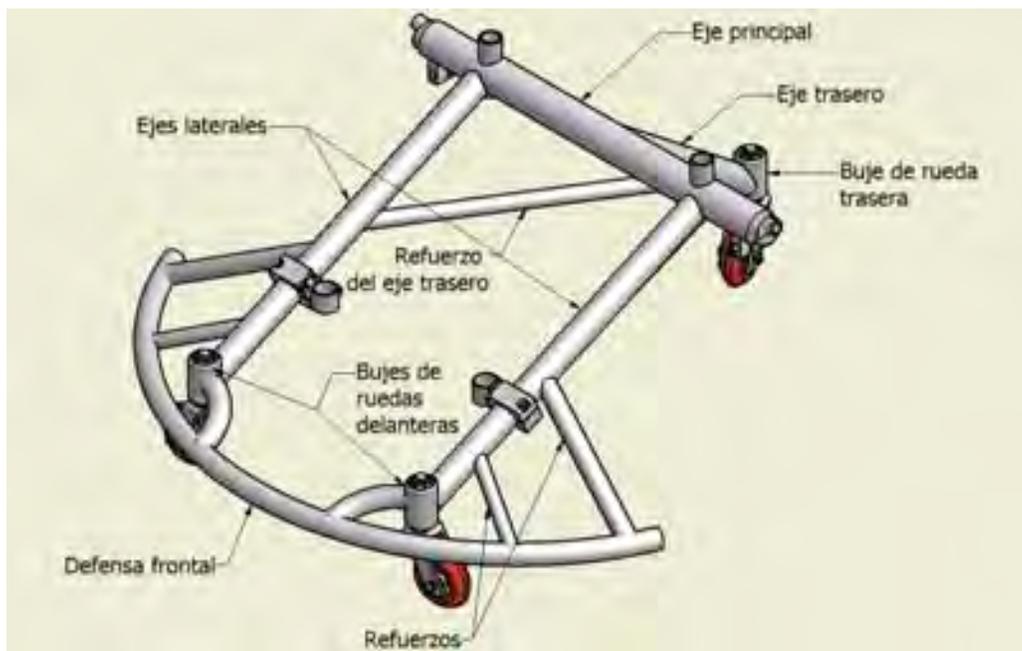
Base principal de la silla de ruedas de balón cesto. Esta estructura se encuentra unida por medio del proceso de soldadura G.T.A.W.
